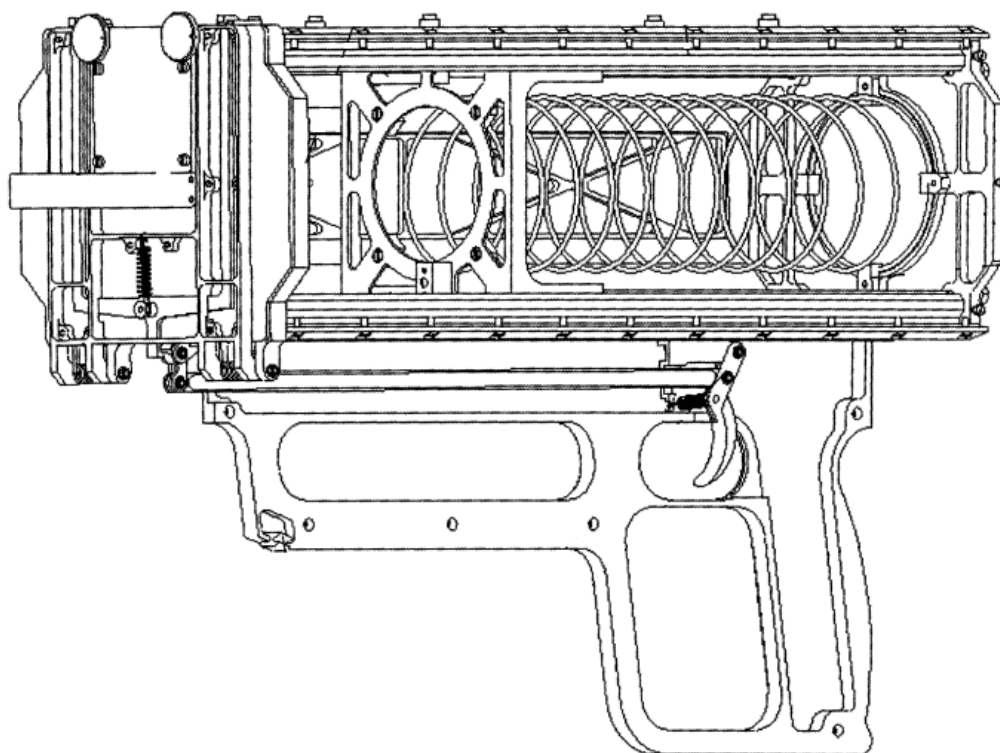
Общий вид ГПК со стороны поворотной крышки
